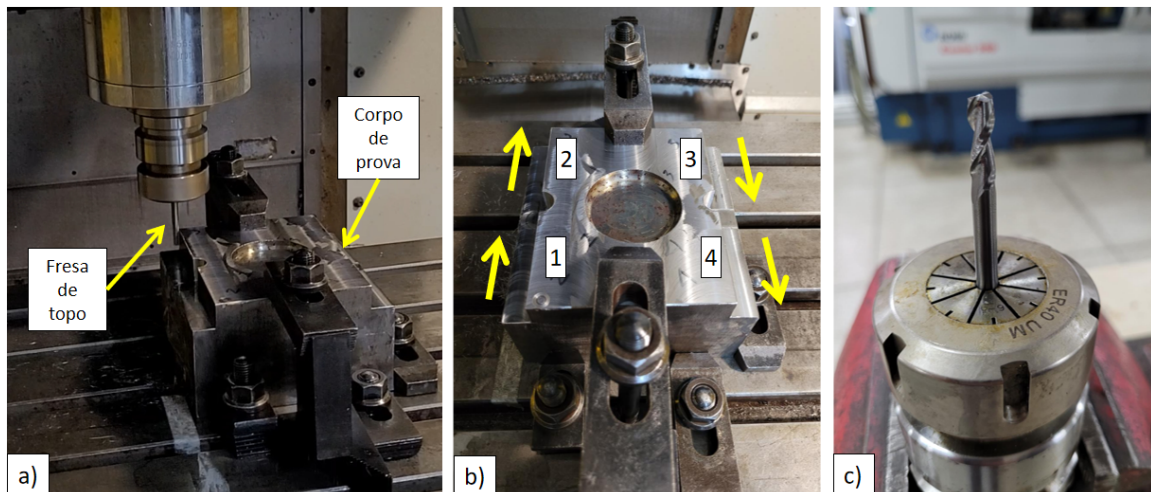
a) Montagem da ferramenta e corpo de prova na máquina-ferramenta, b) superfícies fresadas e sentido de avanço da fresa e c) fresa de metal duro
